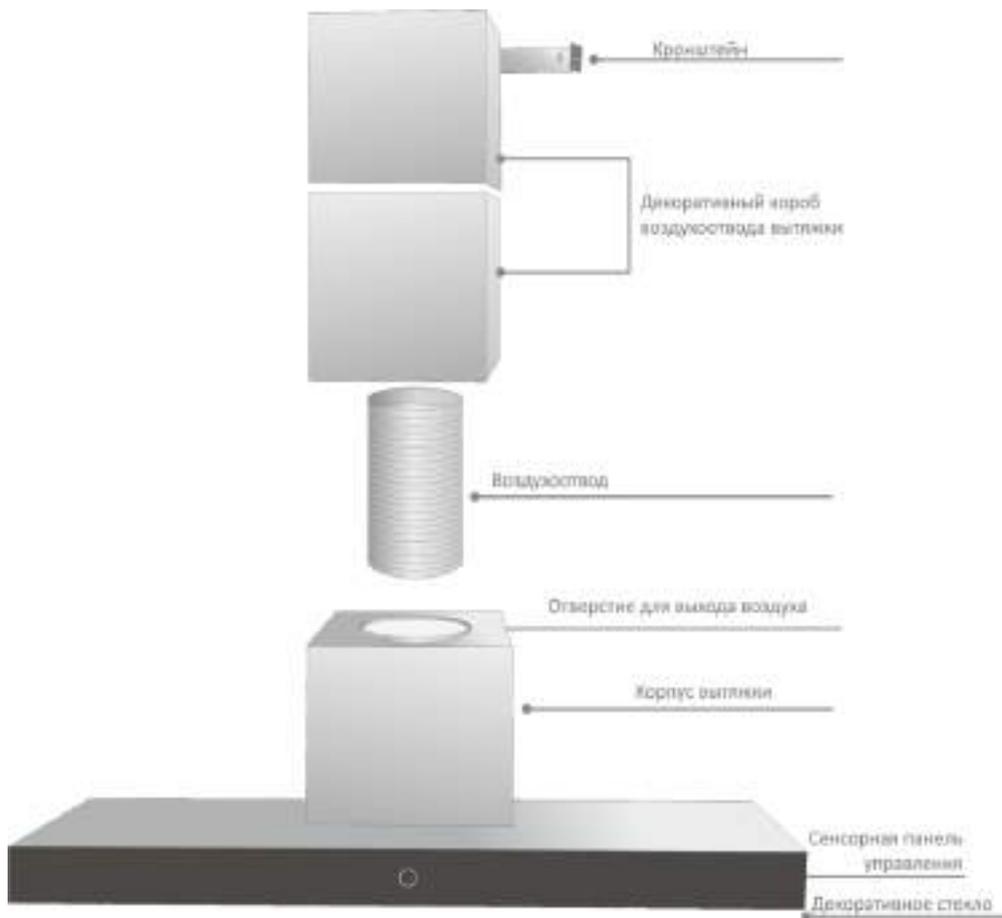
Внешний вид кухонной вытяжки и схема размеров
